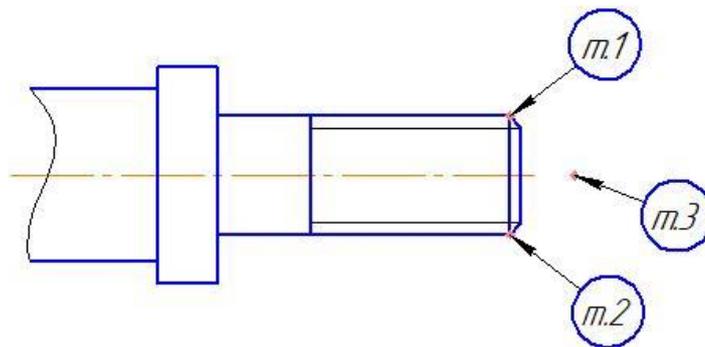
Фрагмент детали с базовыми точками резьбовой поверхности.
